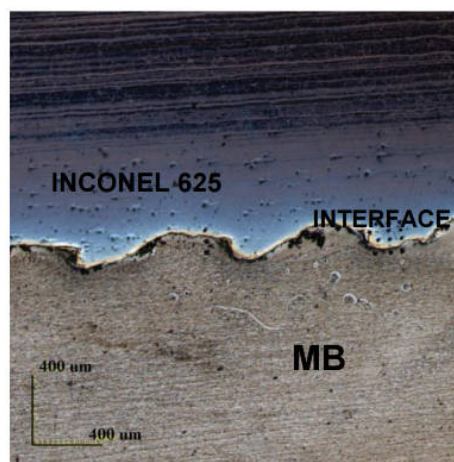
Corte transversal de uma junta soldada por explosão entre um aço API 5L X-65 e Inconel 625. Aumento: 108x. M.O.: Confocal (Ribeiro, 2014).
